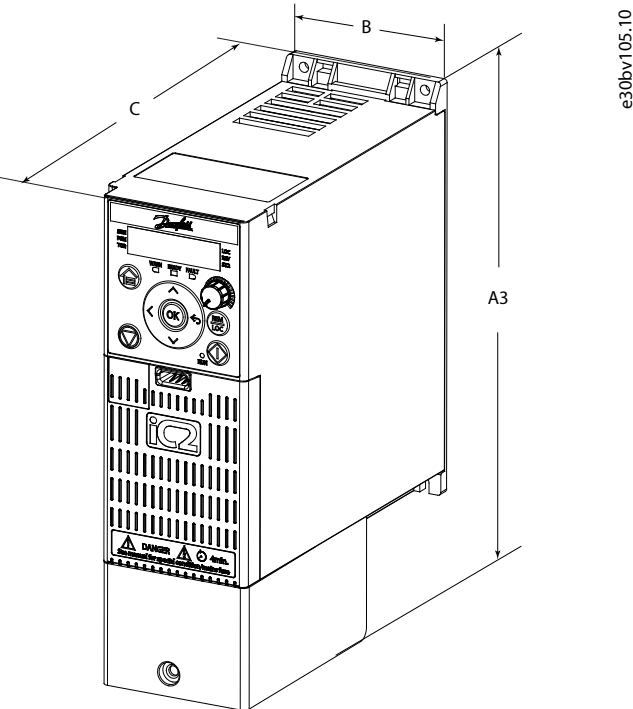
Размери и размер на корпуса на IP21/UL Тип 1
